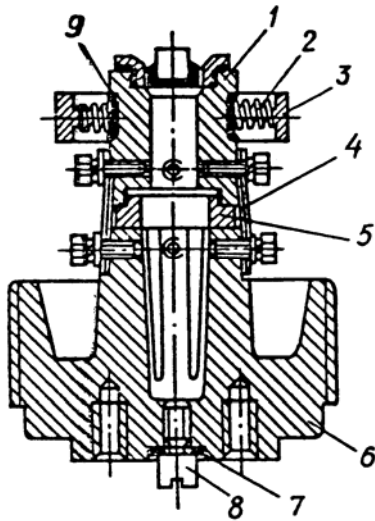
Нерухомий контакт розеткового типу: 1 - ламель; 2 - пружина; 3 - кільце; 4 - гнучке з'єднання; 5 - опорне кільце; 6 - підставка; 7 - ущільнювальне кільце; 8 - оливозливна пробка; 9 - ковпачок
